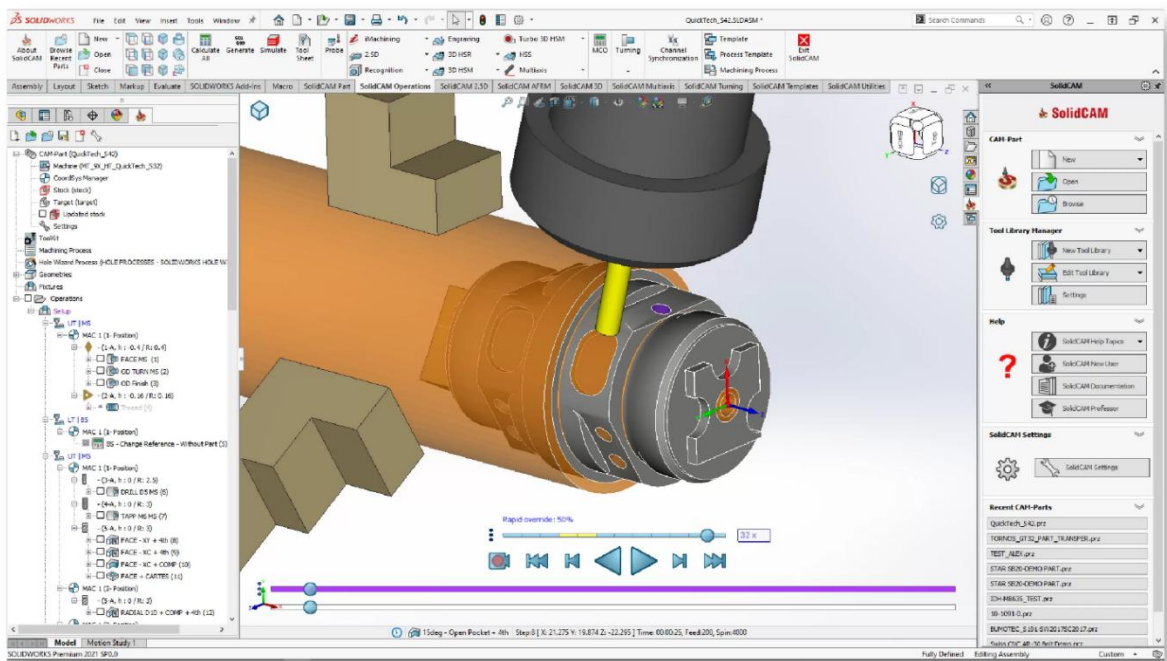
Установ 2 токарна, фрезерна та свердлильна обробка
